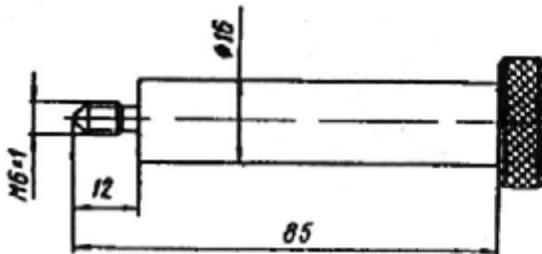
Технологический винт для соединения корпуса поршня со штоком усилителя
